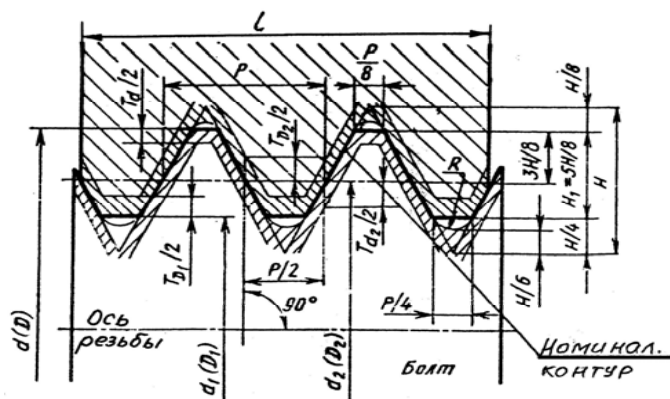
Профиль и предельные контуры резьбового соединения с метрической резьбой при посадке H/h . Основные параметры
